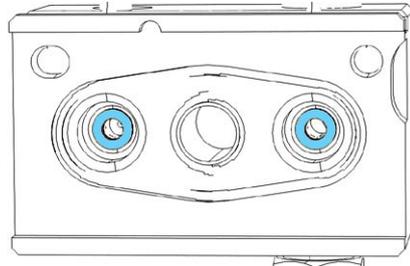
Tête de pompe, joints de piston et bagues de support installés
